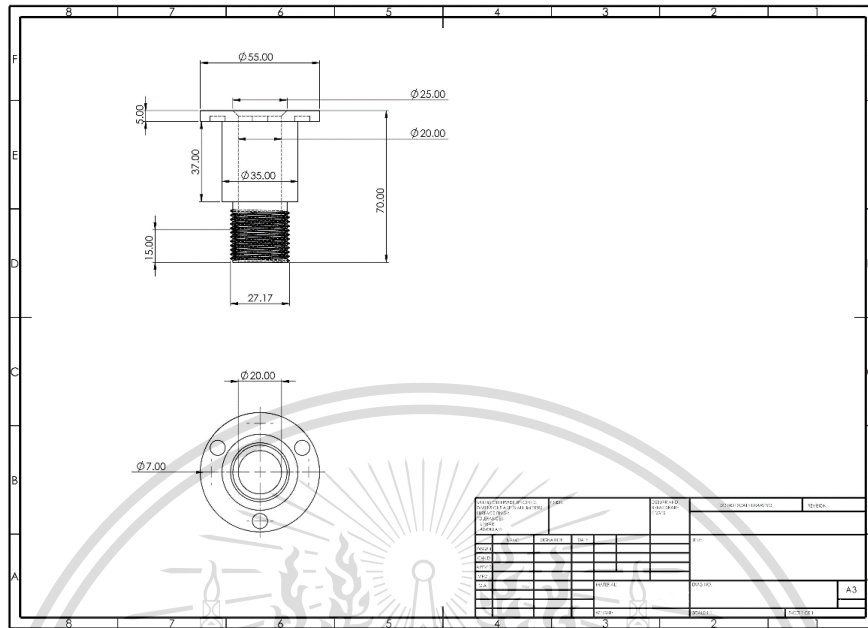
Top – Front – Side View of First Floor Column
